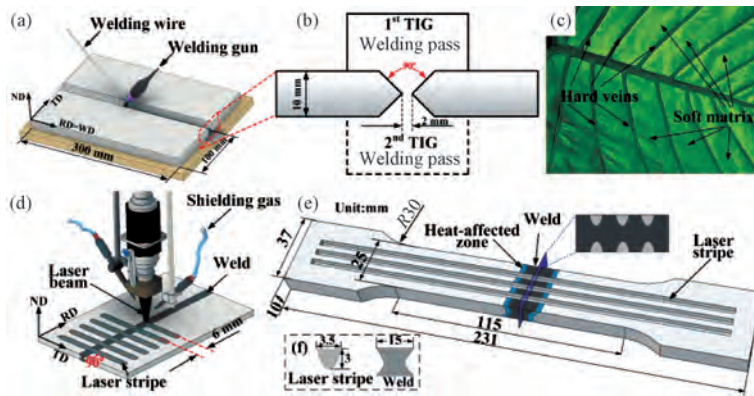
试样加工示意图 (a) TIG 焊接工艺;(b) 焊接坡口尺寸;(c) 仿生原型;(d) 激光加工;
